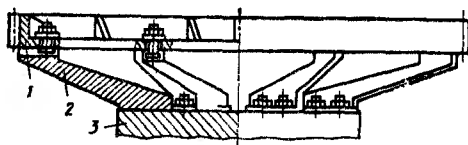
Схема установки заготовки крупного зубчатого колеса на вертикальном зубофрезерном станке:
